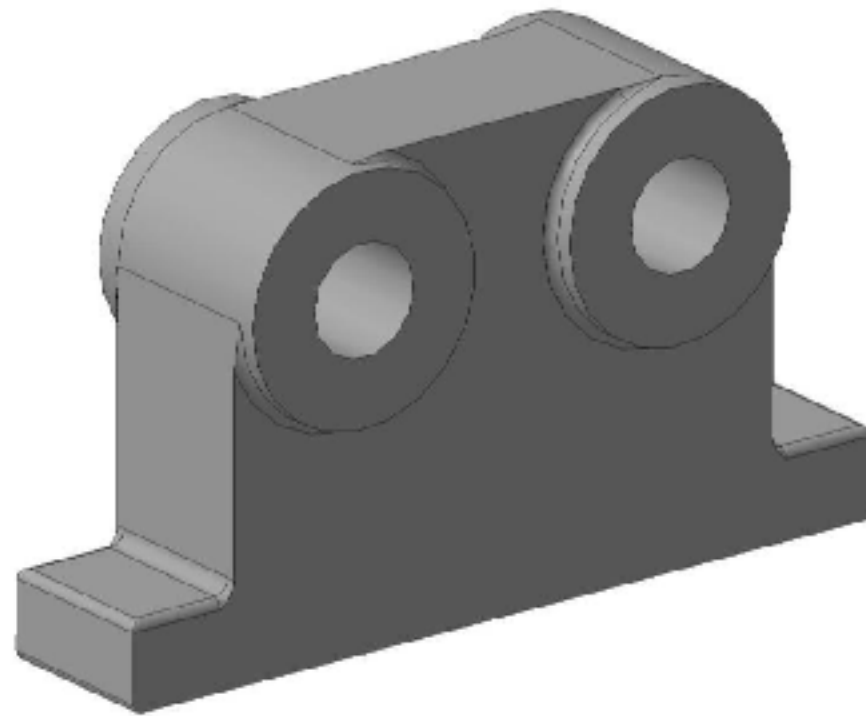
3D-модель заготовки виготовленої литтям в оболонкові форми
